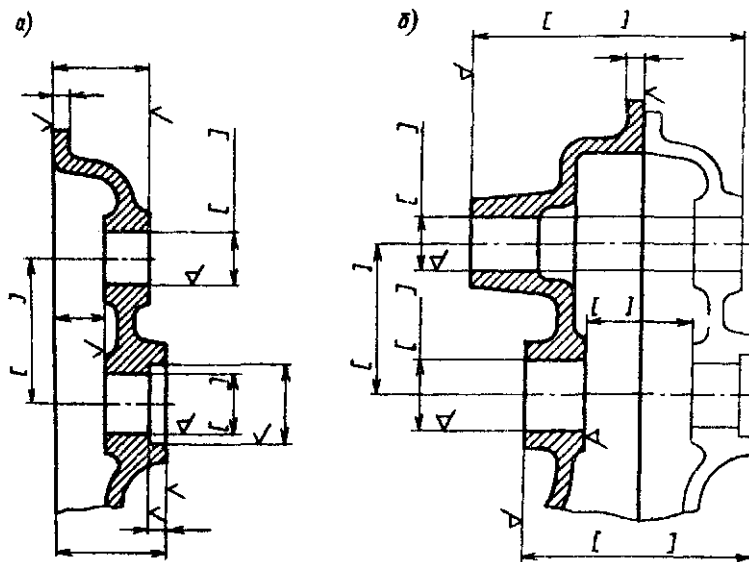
Чертеж деталей, обрабатываемых совместно: *a* — самостоятельный чертеж; *б* — чертеж с изображением другого изделия
